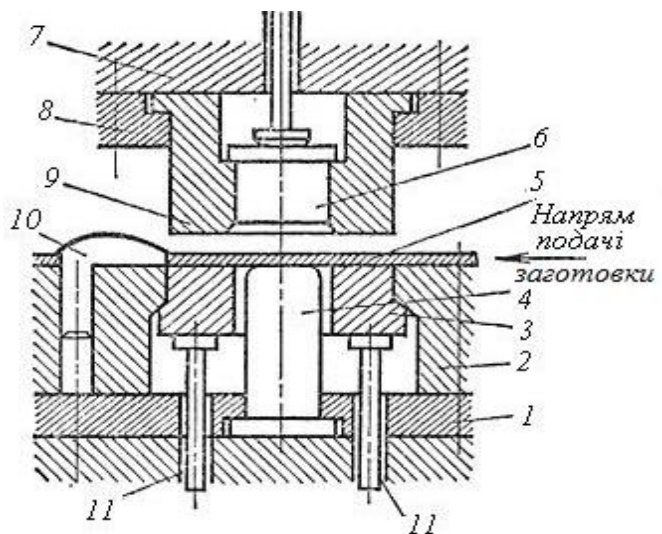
Штамп суміщеної дії: 1 - нижня плита; 2 - матриця вирубку; 3 - притискувач; 4 - пуансон витяжки; 5 - заготовка; 6 - отвір матриці витяжки заготовки; 7 - верхня плита; 8 - тримач пуансона матриці; 9 - матриця пуансона; 10 - обмежувач подачі заготовки; 11 - направляючі кільцевого притискувача 3
